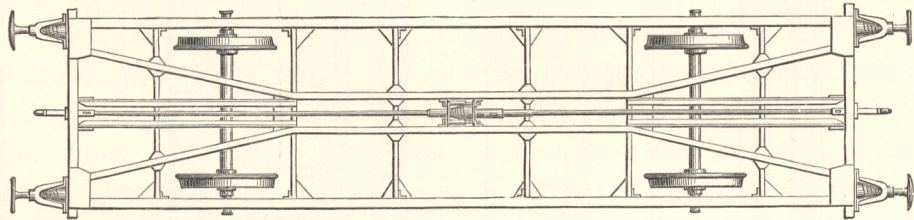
Untergestell mit zwei Achsen und festem Radstand (Grundriß).
